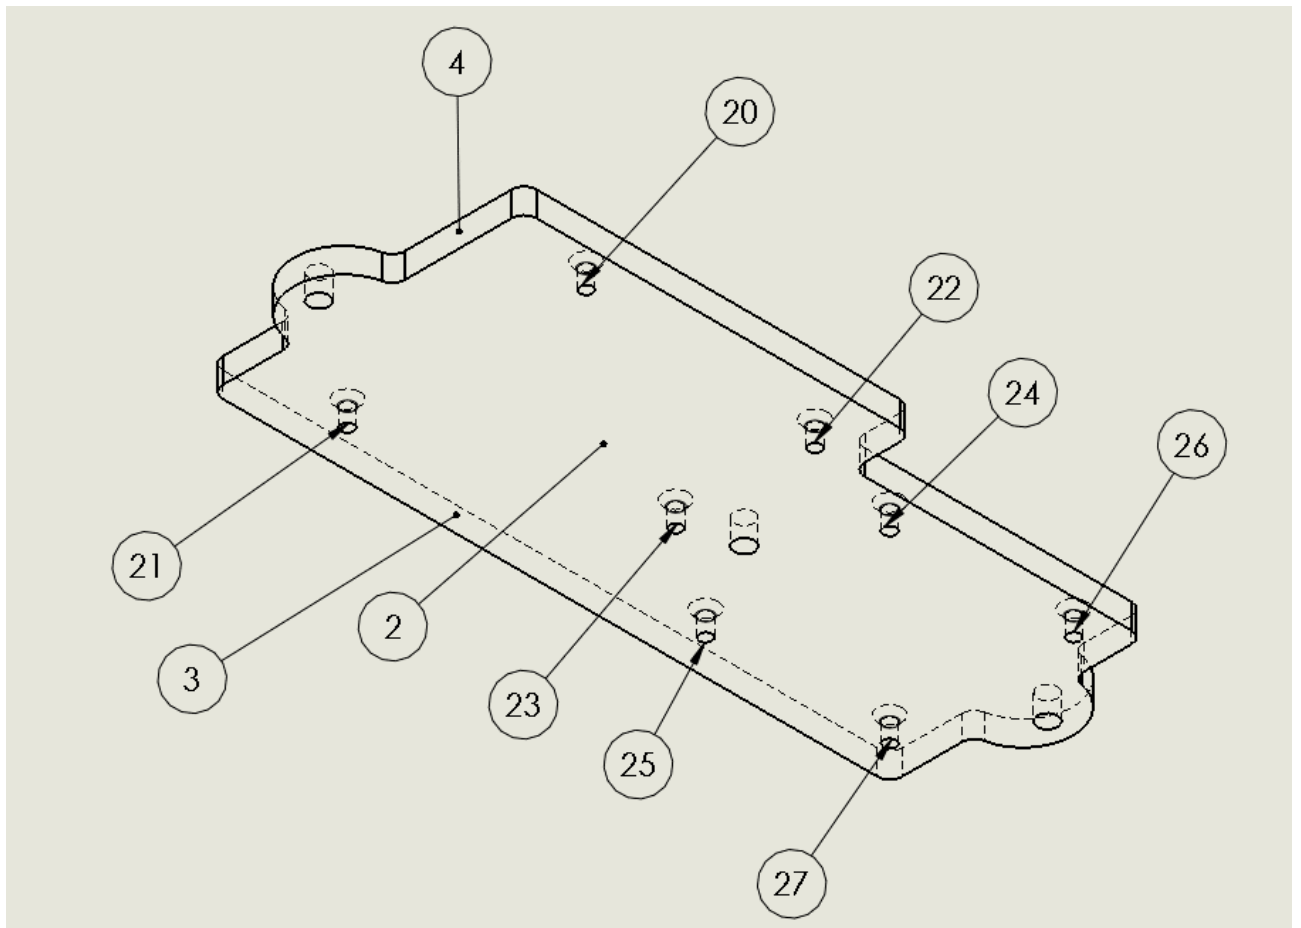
Креслення деталі з поверхнями із сторони закріплення візка
